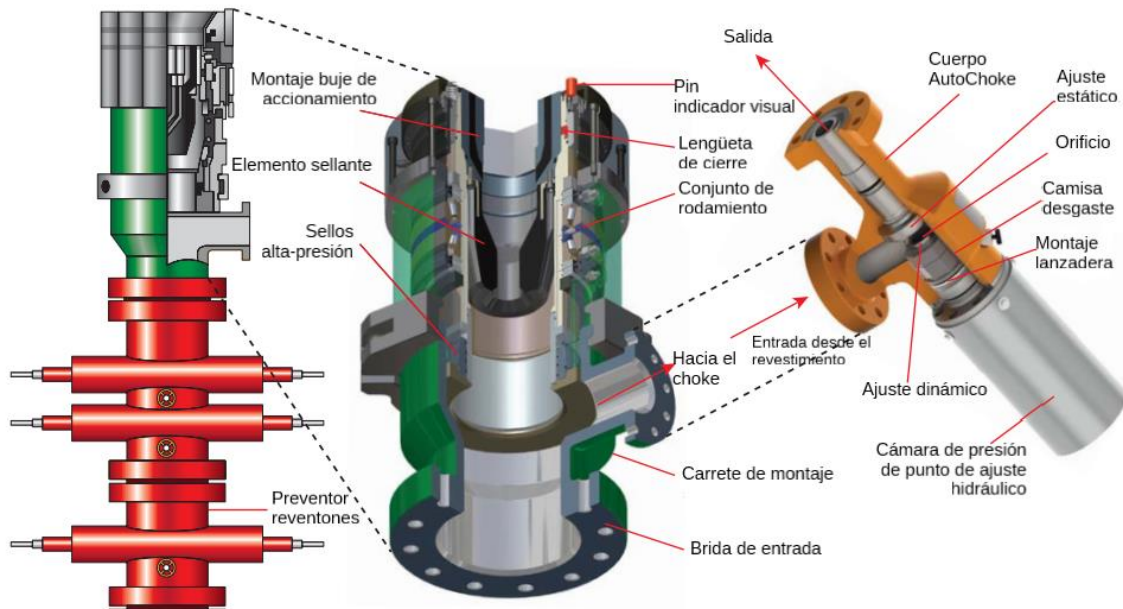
Ensamblaje RCD y Choke Automático sobre BOP
